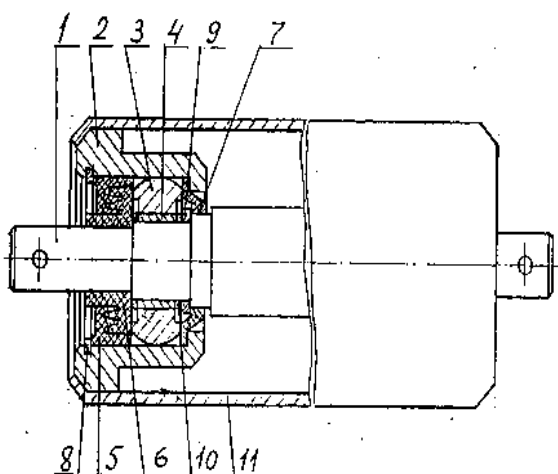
Ролик ленточных конвейеров с металлофторопластовыми подшипниками скольжения
